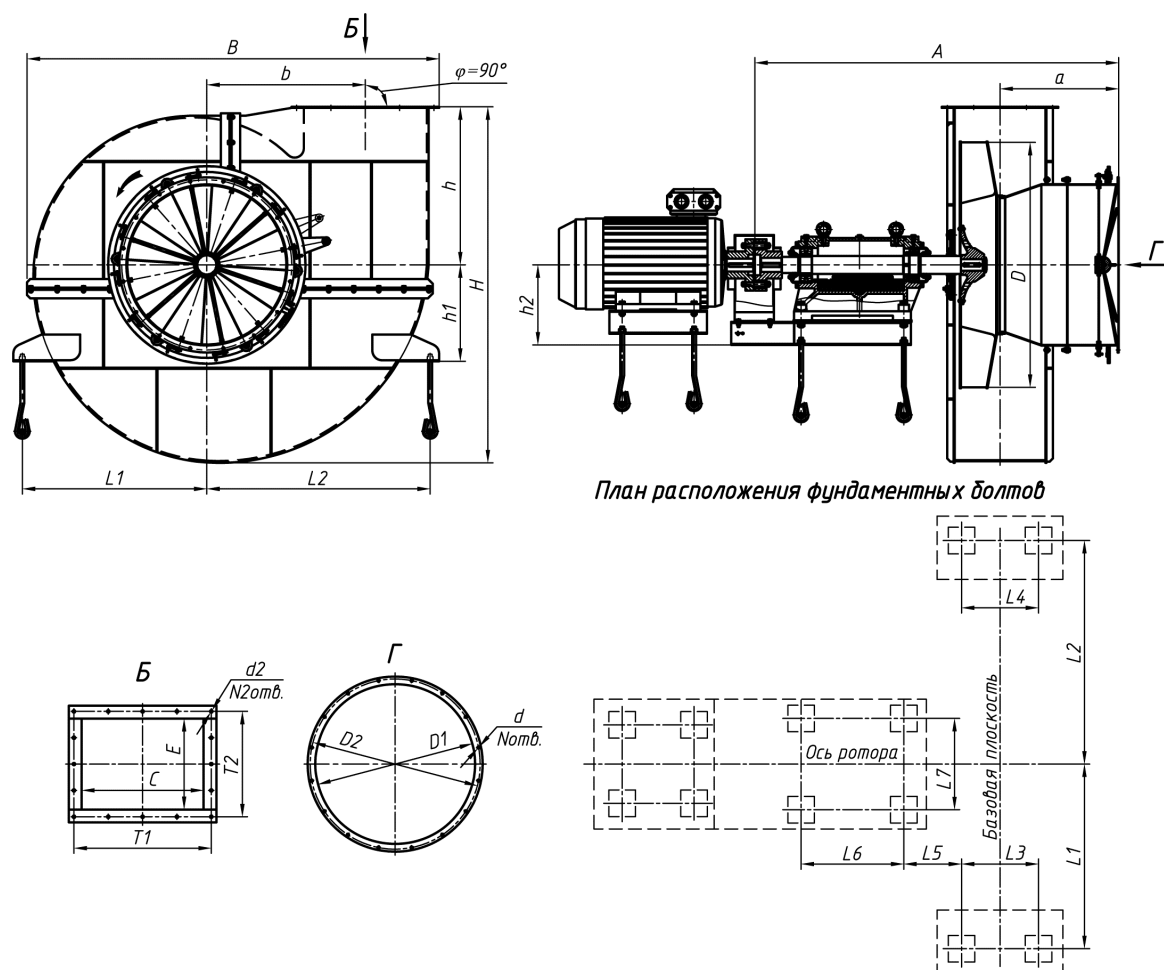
Габаритные и присоединительные размеры центробежных тягодутьевых машин исполнения 3 ВД, Д №13,5-20
